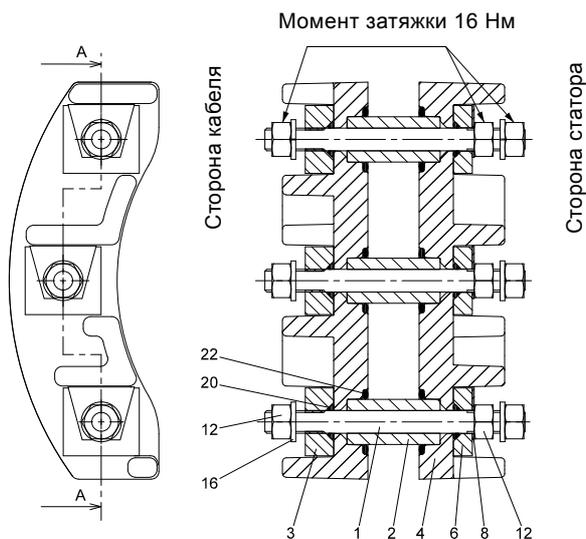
Стандартная клеммная колодка, типоразмер 72
